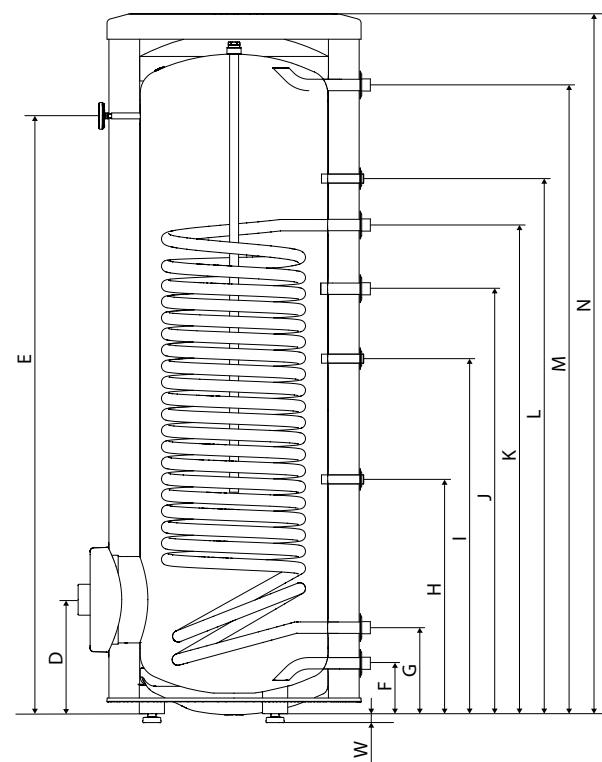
Dimensioner på BA-ST 3022/3030 - 1F varmtvandsbeholder
